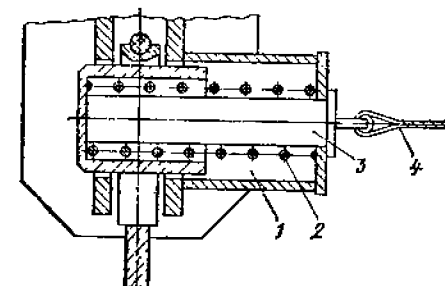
Штырьевой замок с управлением тяговым магнитом: 1 — корпус замка; 2 — пружина; 3 — палец; 4 — тяговый тросик
